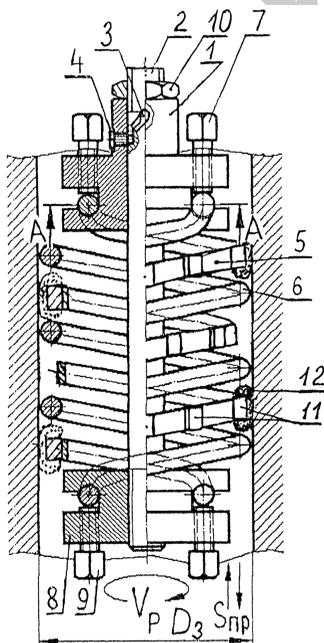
Схема обработки отверстия предлагаемым инструментом и частичный продольный разрез инструмента
